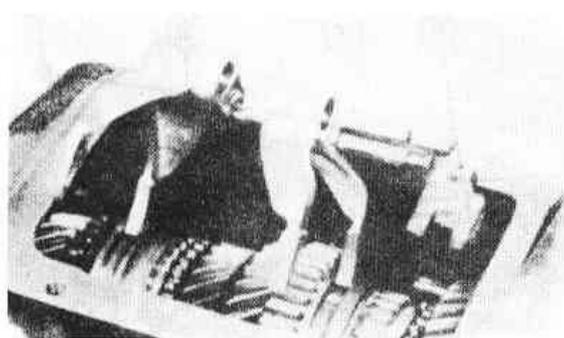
Установка вилок включения передач коробки типа С (Разд.7)
